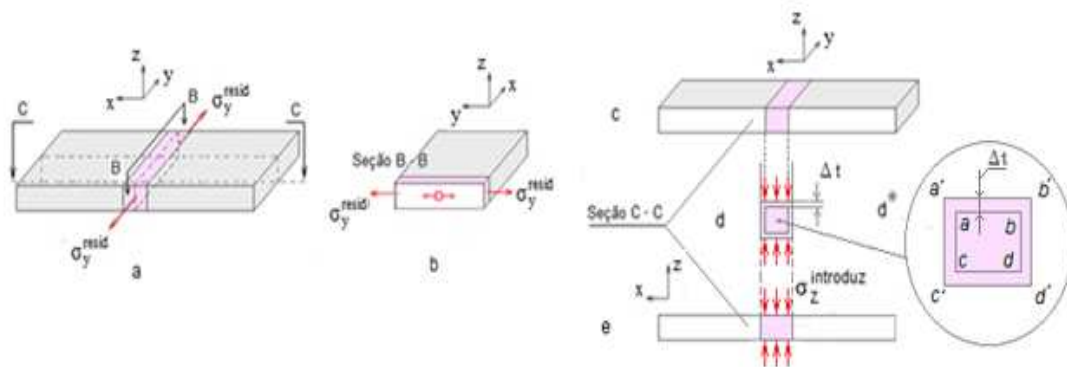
Tensões residuais no cordão de solda e seções de corte por planos paralelos e perpendiculares ao cordão (a – vista geral das chapas soldadas com planos de corte; b – tensão residual na seção transversal B – B; c – seção transversal C – C; d, d\* – alta)
